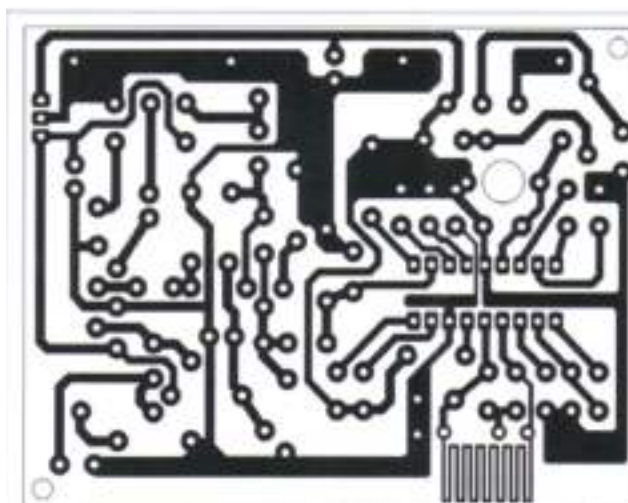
Circuito impresso do recetor FM, visto pelo lado das pistas de cobre.
